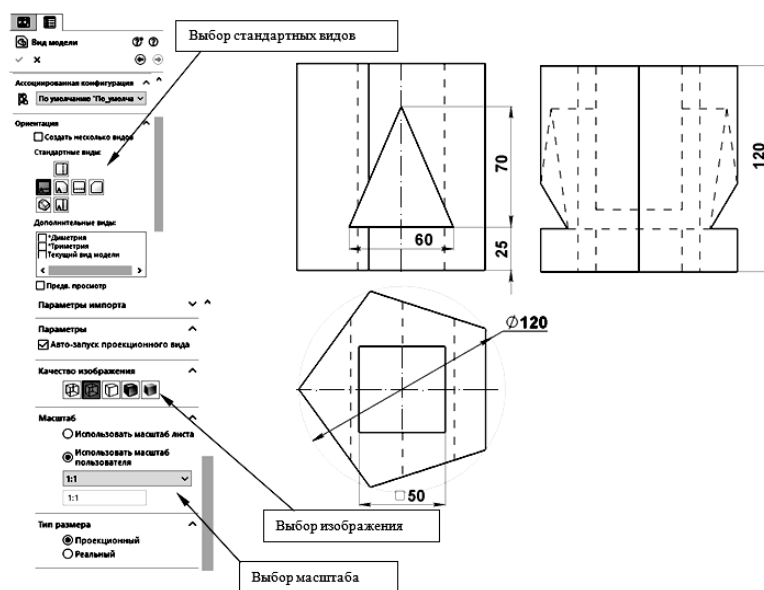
Двумерный чертеж детали на основе трехмерной модели в SolidWorks
